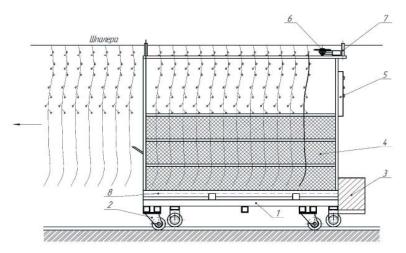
Схема машины для уборки растительных остатков: 1 – рама; 2 – колеса опорные; 3 – электропривод; 4 – бункер; 5 – пульт управления; 6 – режущий элемент; 7 – ролики направляющие; 8 – платформа подъемная
